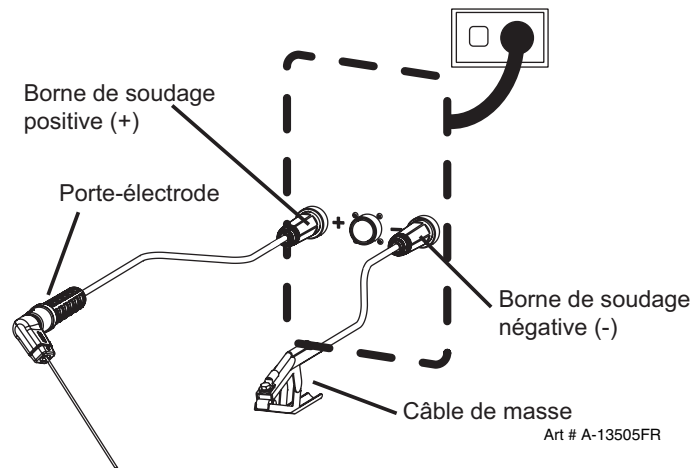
Configuration pour soudage à l'électrode enrobée (procédé SMAW)
